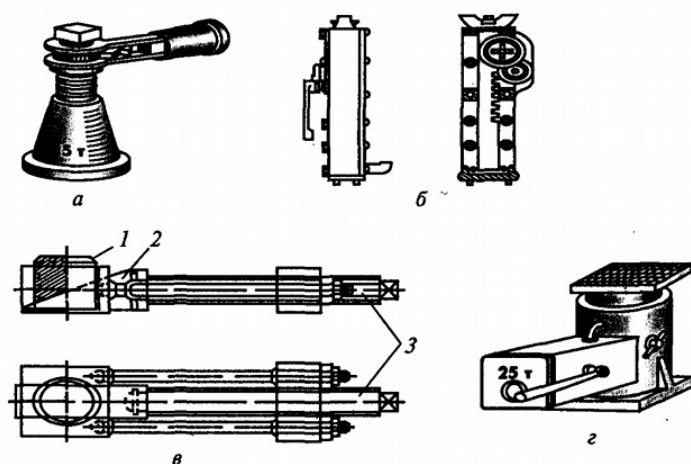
Домкраты: а — винтовой; б — с зубчатой рейкой; в — клиновой; г — гидравлический; 1 — опора; 2 — клин; 3 — винт
